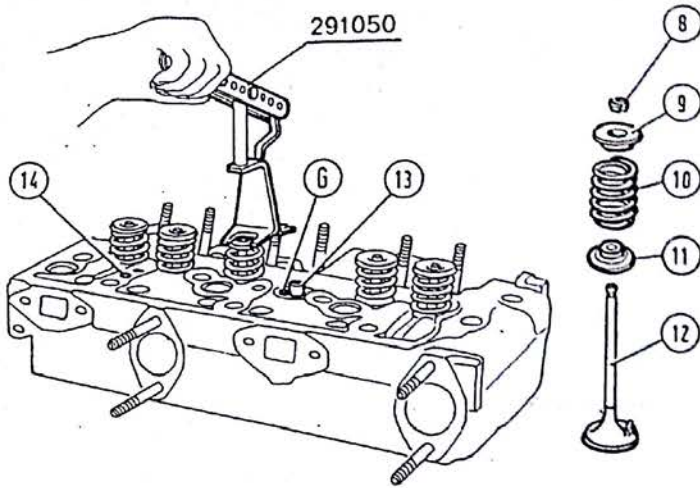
/17 - Démontage (Remontage) des ressorts et des soupapes avec l'outil 291 050.
